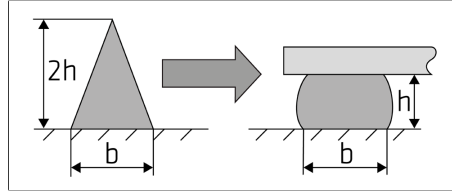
Comprimerne il cordolo adesivo alla dimensione finale
